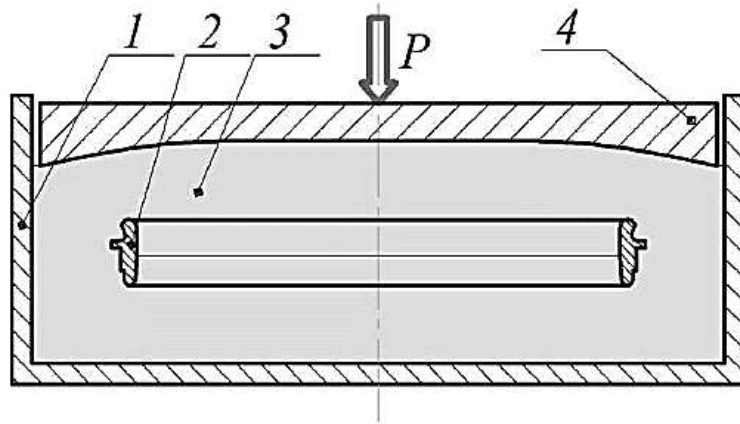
Принципова схема пристрою для ізостатичного пластичного деформування: 1 – робоча камера; 2 – деталь; 3 – сферичні індентори; 4 – поршень
